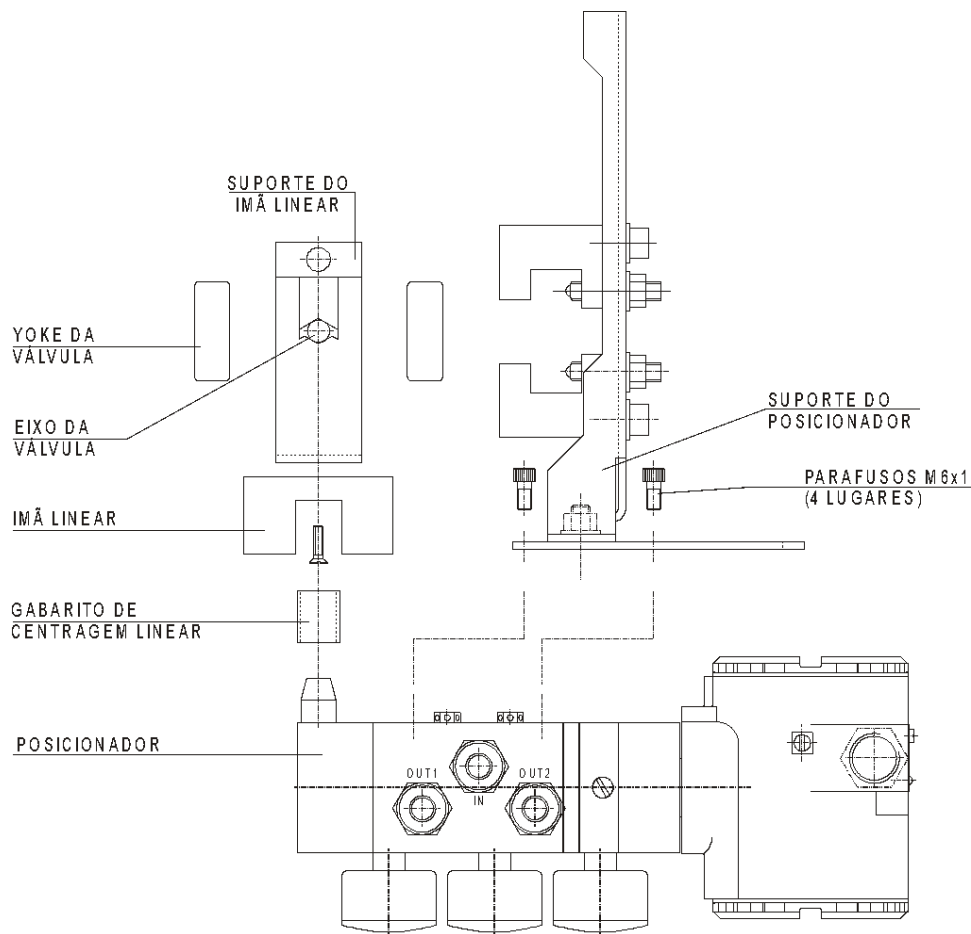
Esquema de Montagem do Posicionador em Atuador Linear
